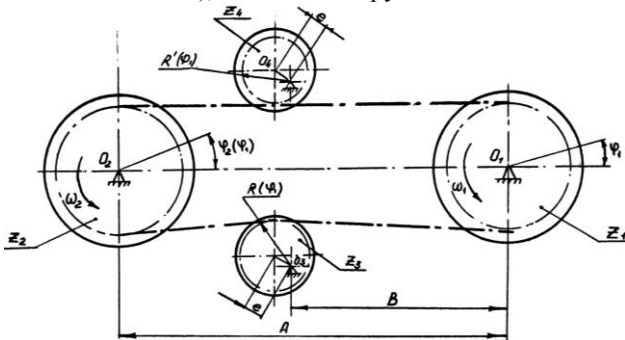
Схема цепного замедлителя для жаккардовой машины
